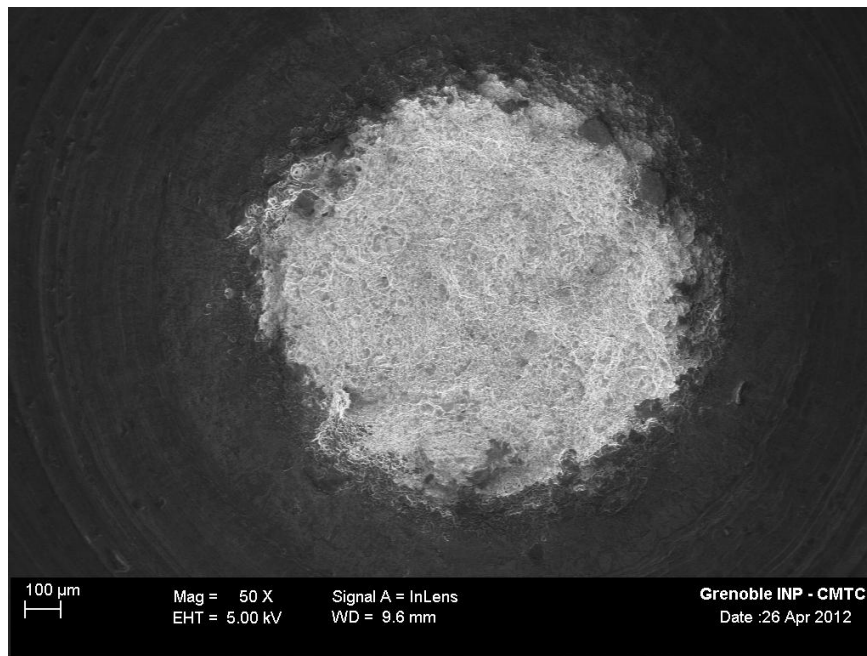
Fractografía de la probeta cilíndrica ASTM, con entalle en 90°, de cobre comercial 99,99%. Se muestra la zona de fractura que se localiza en el entalle.
